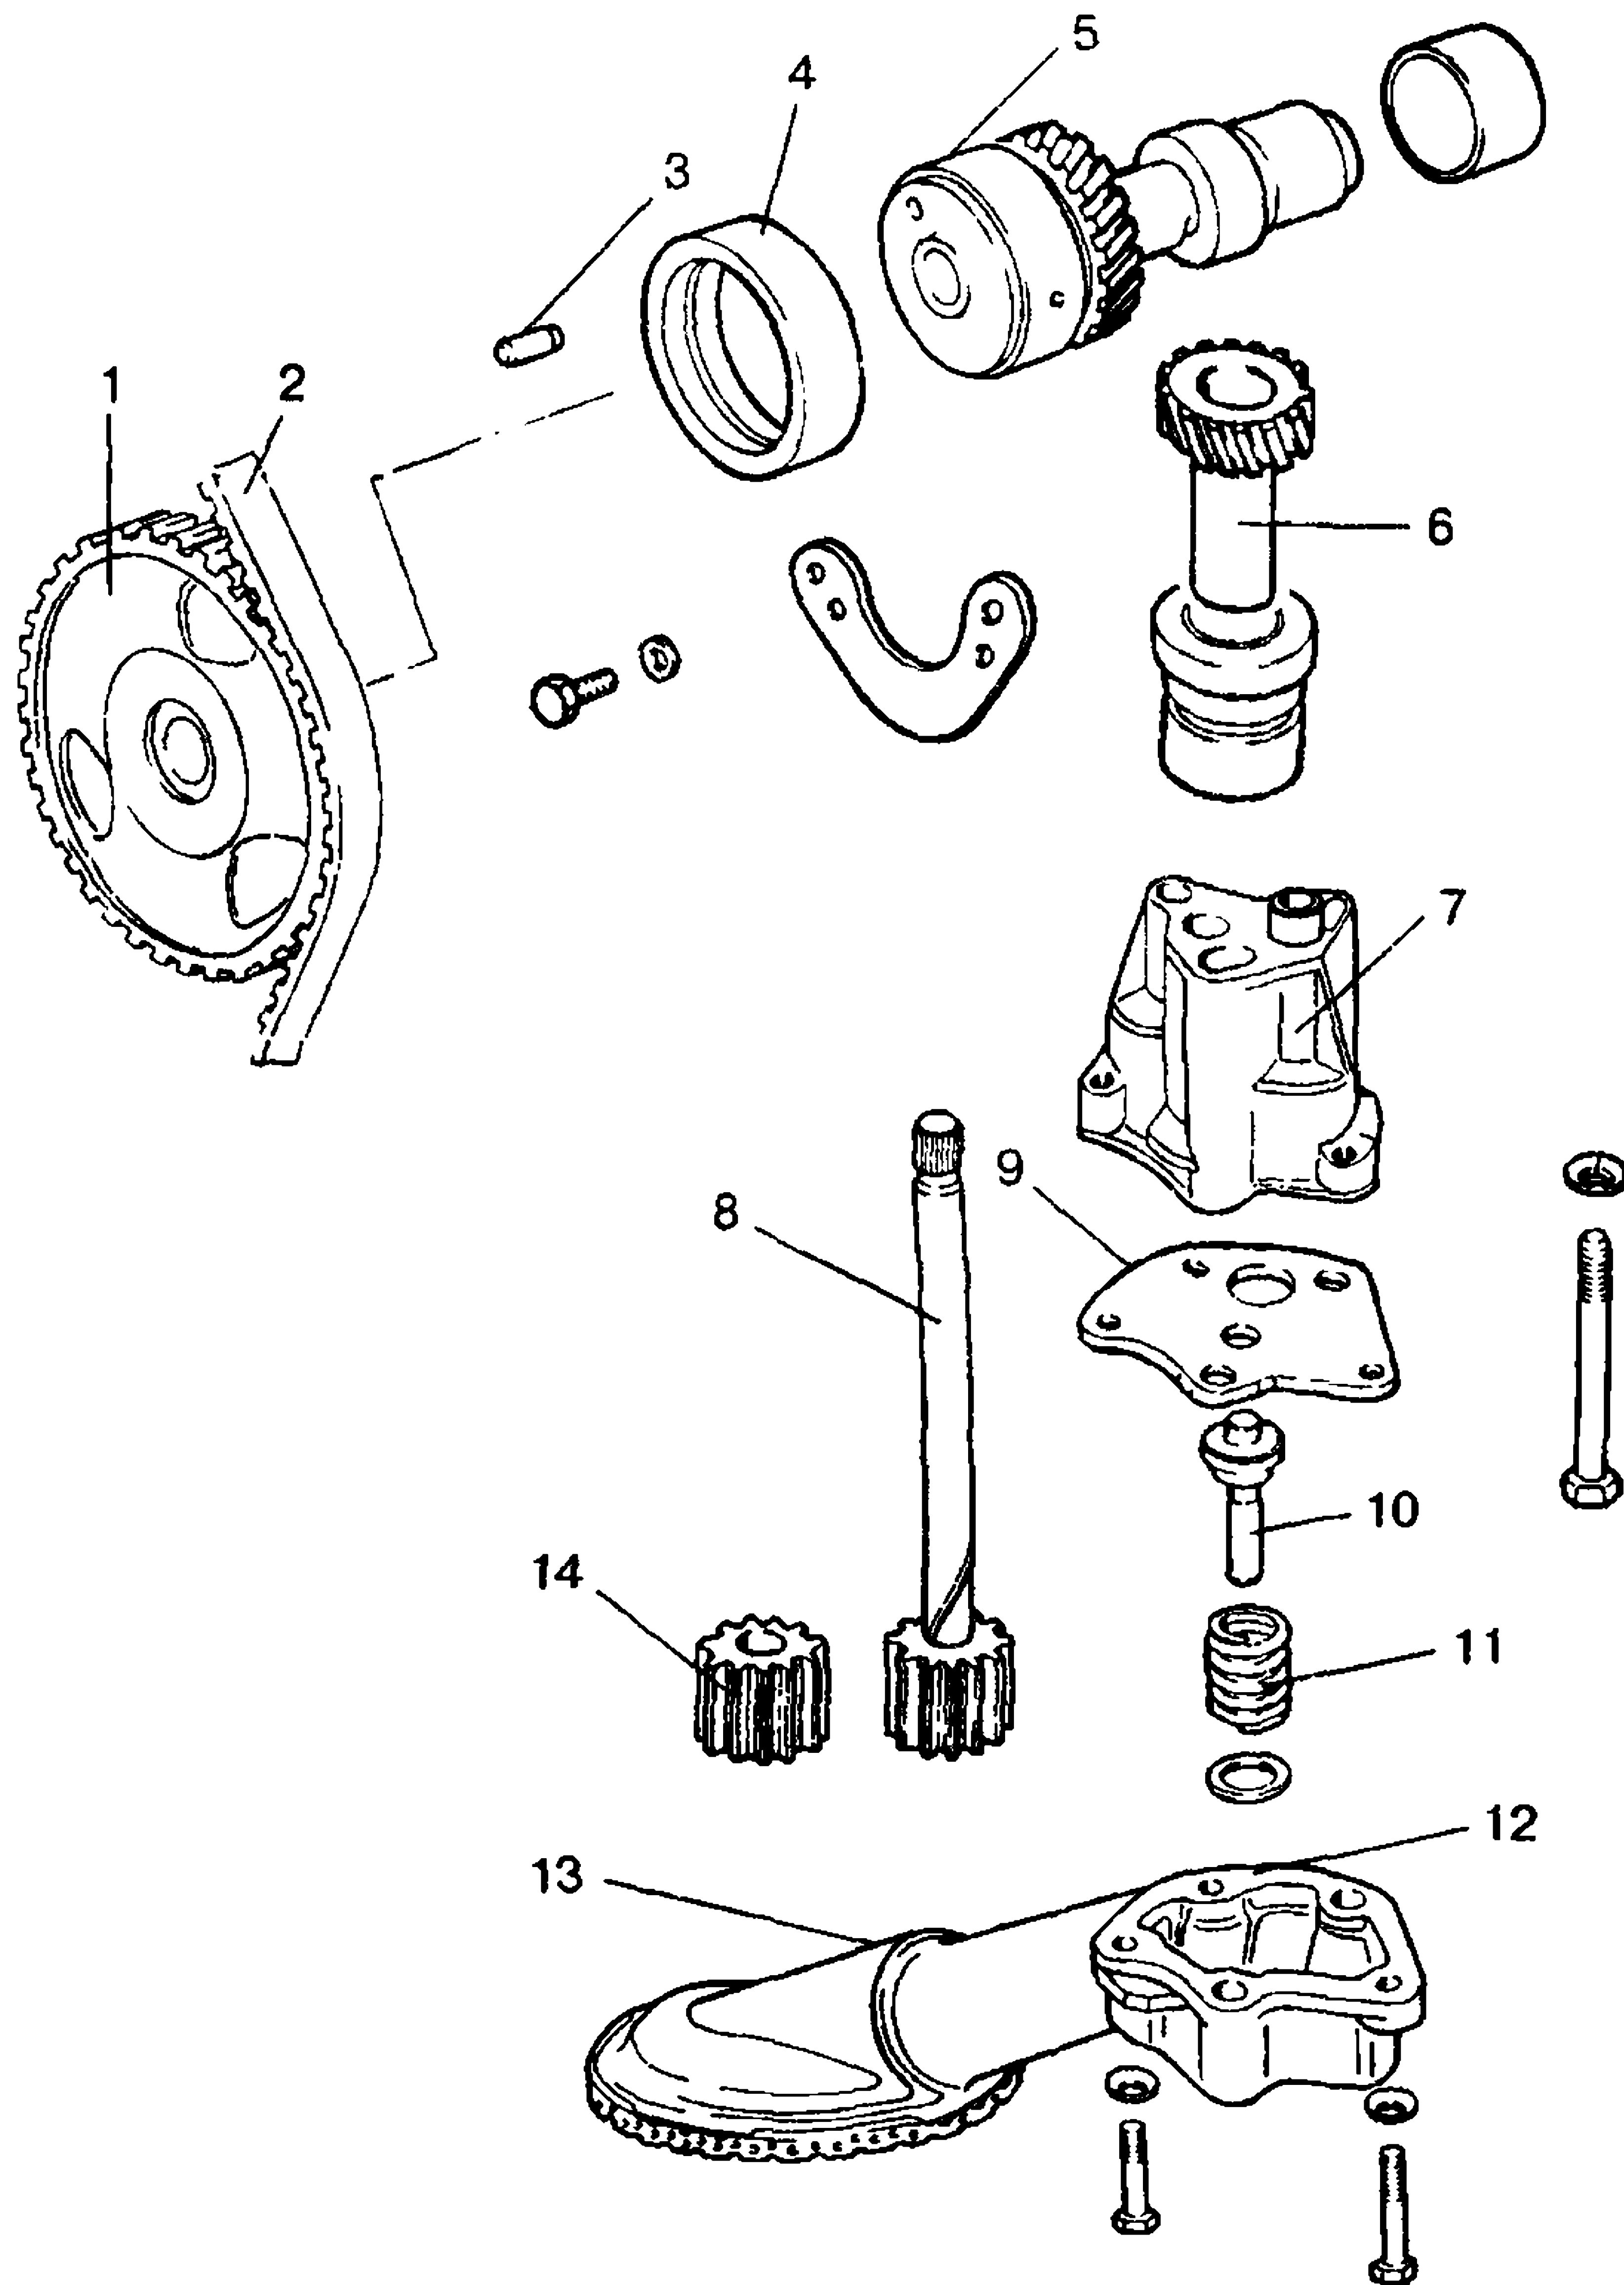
Детали маслонасоса двигателей с цепным приводом распредвала и двигателя 2105:
